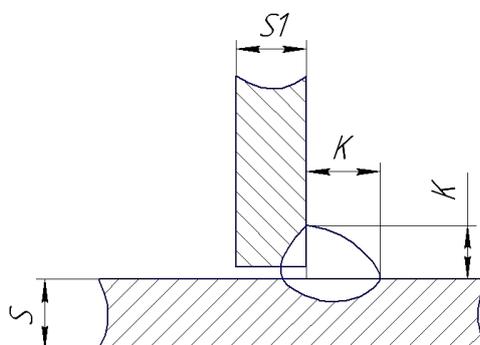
Схема сварочного шва Т1-Δ5 согласно ГОСТ 14771-76
